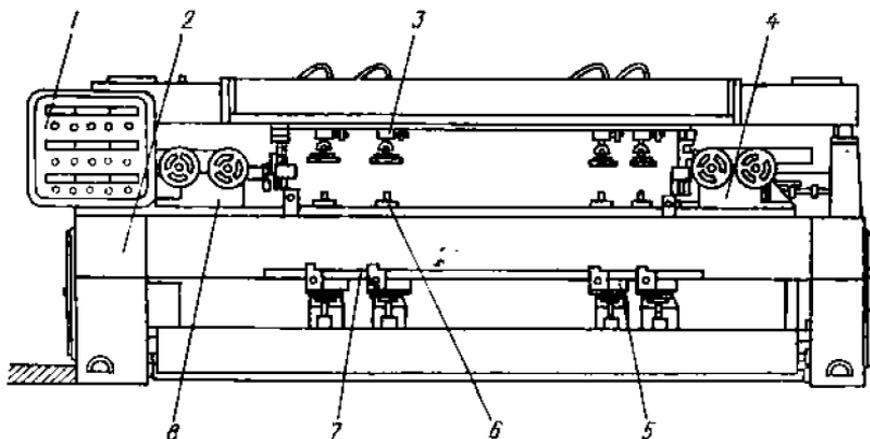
Станок сверлильный многошпиндельный, горизонтально-вертикальный СГВП-1А с загрузочно-разгрузочным устройством
